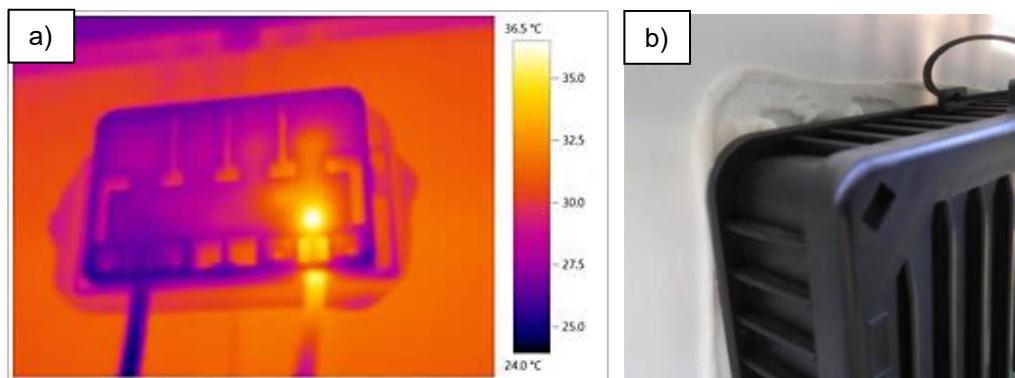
Termografia de uma caixa de junção com sobreaquecimento devido a má soldagem [87]; b) Caixa de junção mal fixada [81].
